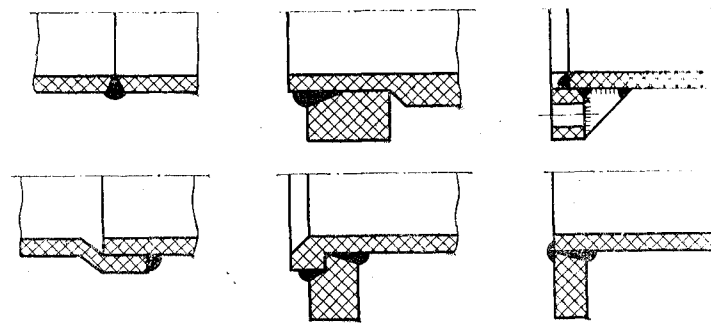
Типовые конструкции сварных фланцев и труб
